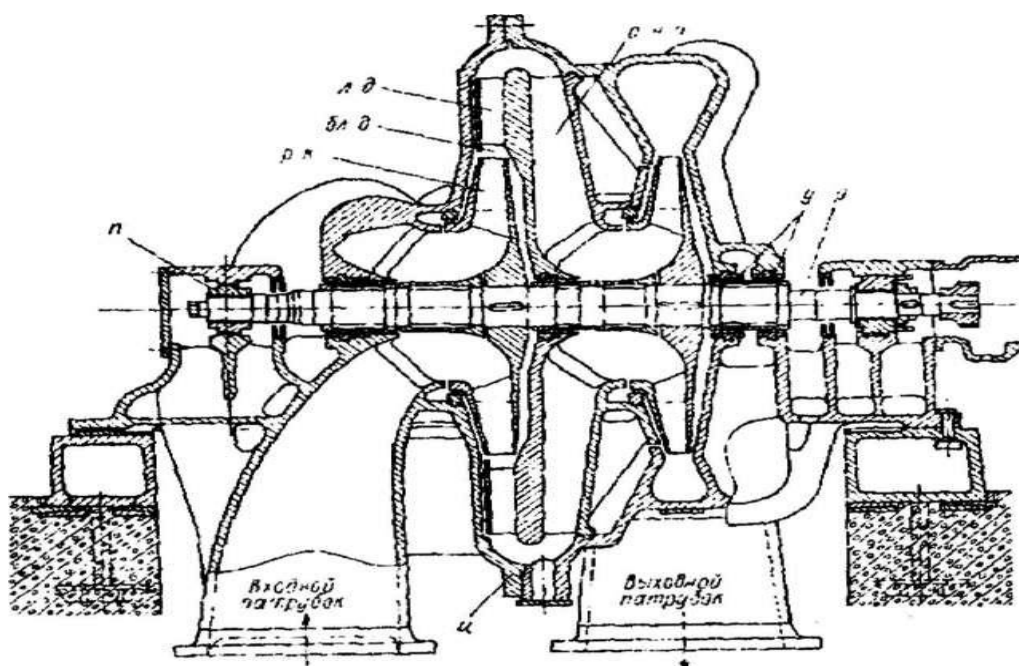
Центробежный компрессор: ЛД - лопаточный диффузор; БЛД - безлопаточный диффузор; ОНА - обратный направляющий аппарат; Р - ротор
